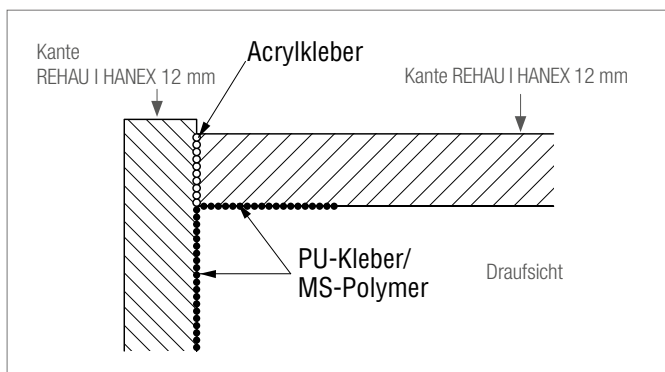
Kante anbringen (REHAU I HANEX 10 mm)
